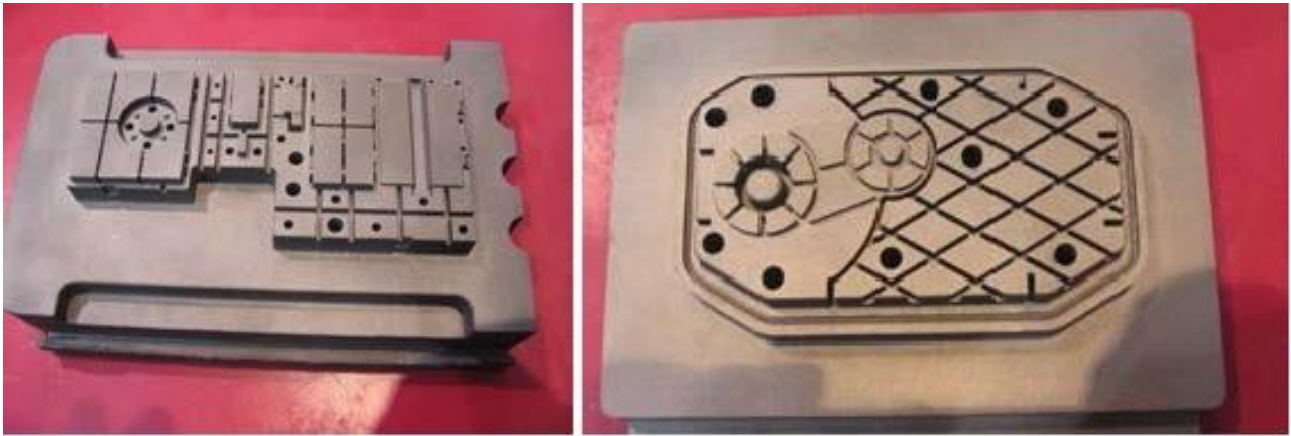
Синтезированные металлические вставки для литья деталей из пластмассы (3D Systems)
